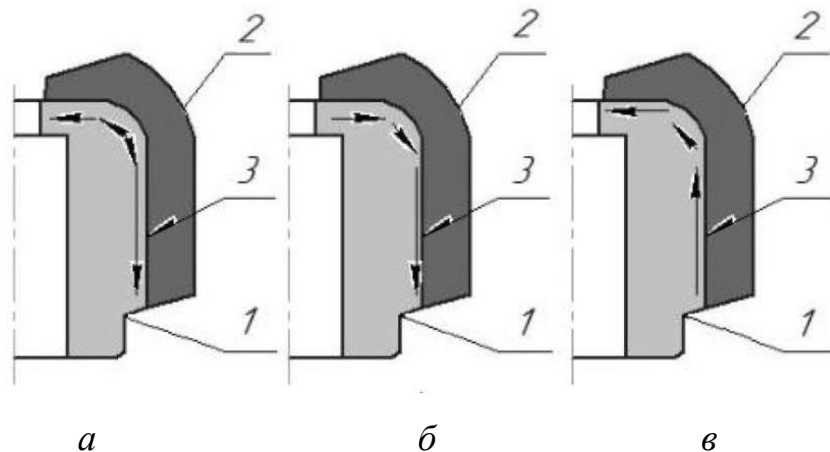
Різні схем формування зварних швів у корпусі:
